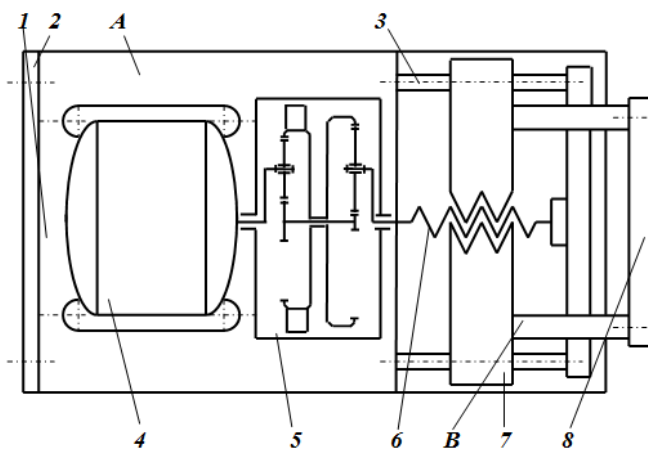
Конструктивная схема адаптивного привода схвата робота на основе зубчатого адаптивного механизма, с модулем поступательного движения
